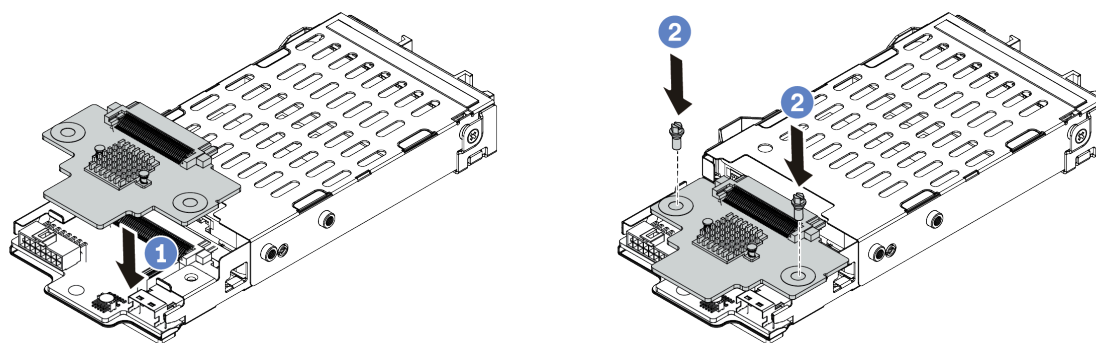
Installation d'un fond de panier d'unité 7 mm (haut)
